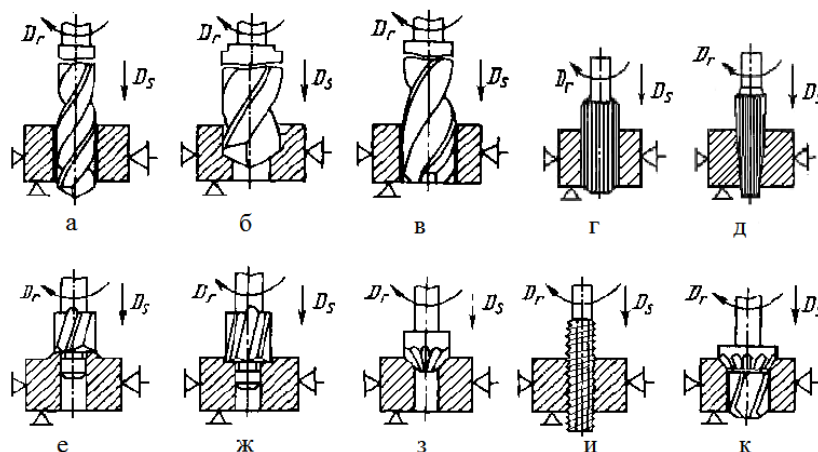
Схемы обработки заготовок осевым многолезвийным инструментом: а – сверление; б – рассверливание; в – зенкерование; г, д – развертывание соответственно цилиндрического и конического отверстия; е, ж – цекование; з – зенкование; и – нарезание резьбы; к – обработка отверстия сложного профиля комбинированным инструментом (комбинированный зенкер)
